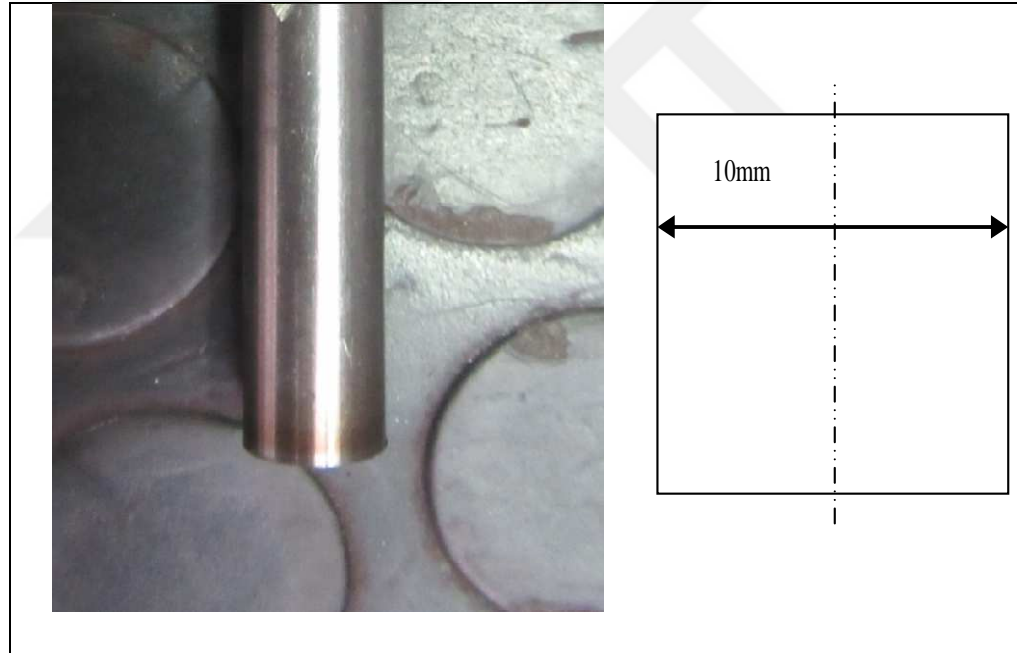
İşlenmiş FSSW takımı malzemesi
